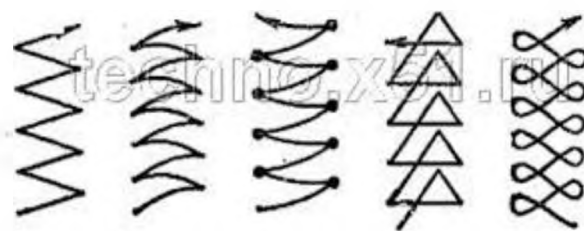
Траектория движения конца электрода при ручной дуговой сварке
